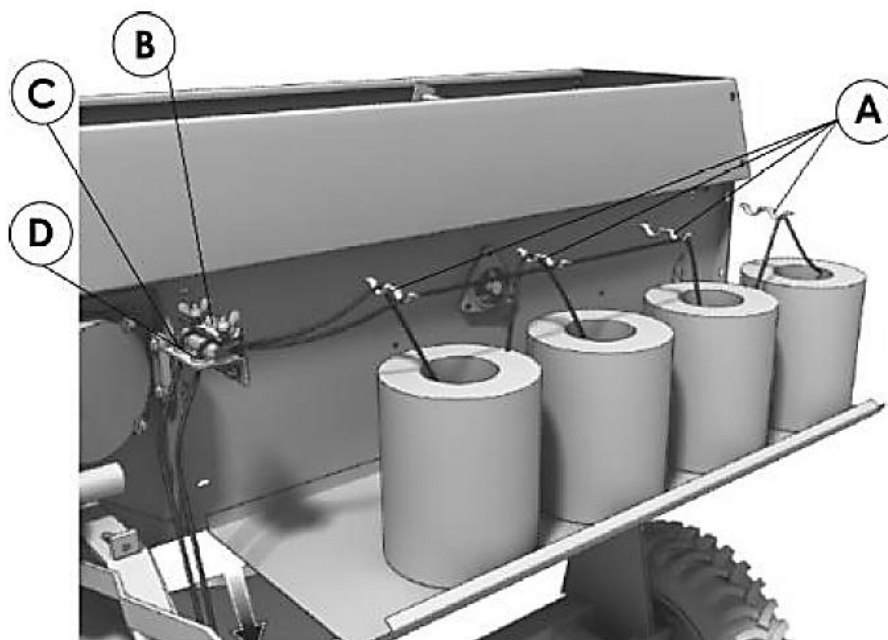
Установка бухт шпагата: А – верхние проушины; В – механизм натяжения шпагата; С и D – отверстия
